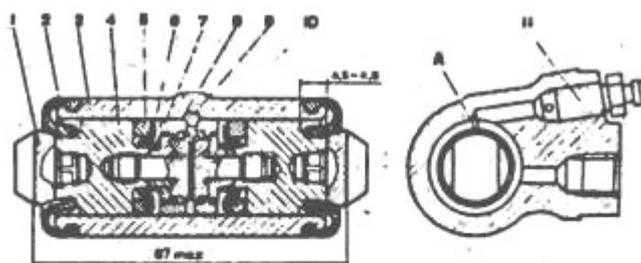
Колесный цилиндр: 1 - упор колодки; 2 - защитный колпачок; 3 - корпус цилиндра; 4 - поршень; 5 - уплотнитель; 6 - опорная чашка; 7 - пружина; 8 - сухари; 9 - упорное кольцо; 10 - упорный винт; 11 - штуцер; А - прорезь на упорном кольце
